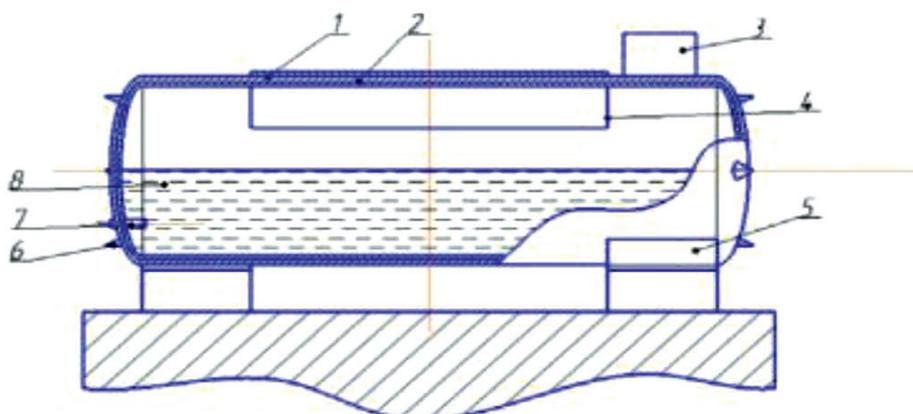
Схема крематора: 1 – корпус крематора, 2 – ТЗП, 3 – труба, 4 – крышка, 5 – крепление крематора, 6 – ножки, 7 – воспламенитель, 8 – биологические отходы
